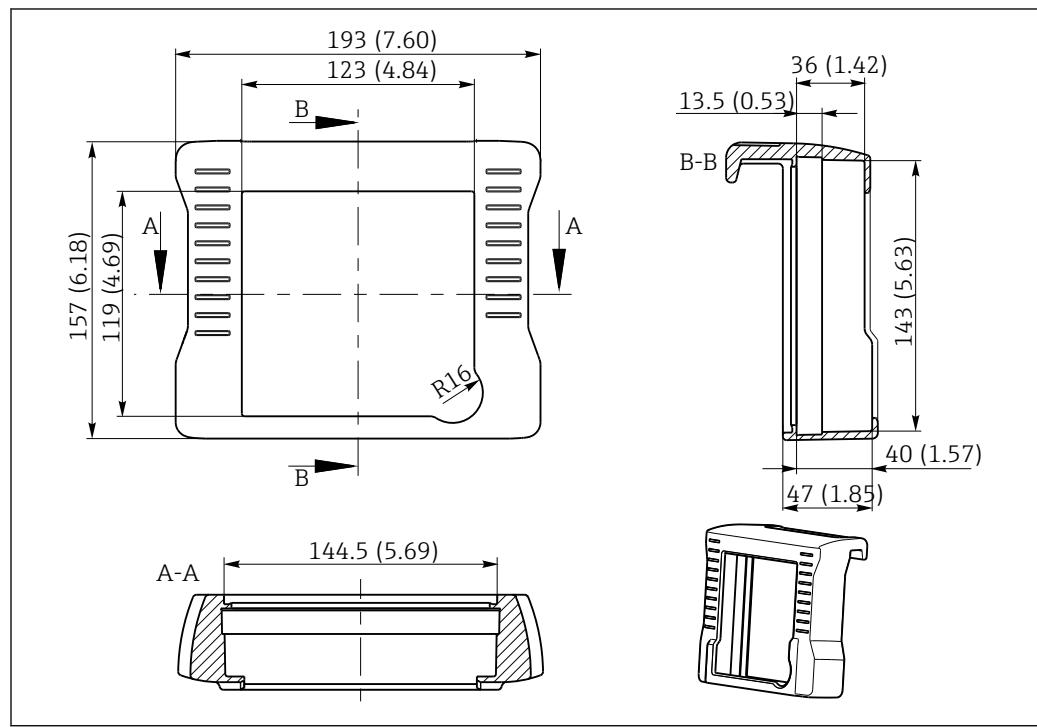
Dimensiones de la tapa del indicador de servicio en mm (pulgadas)
